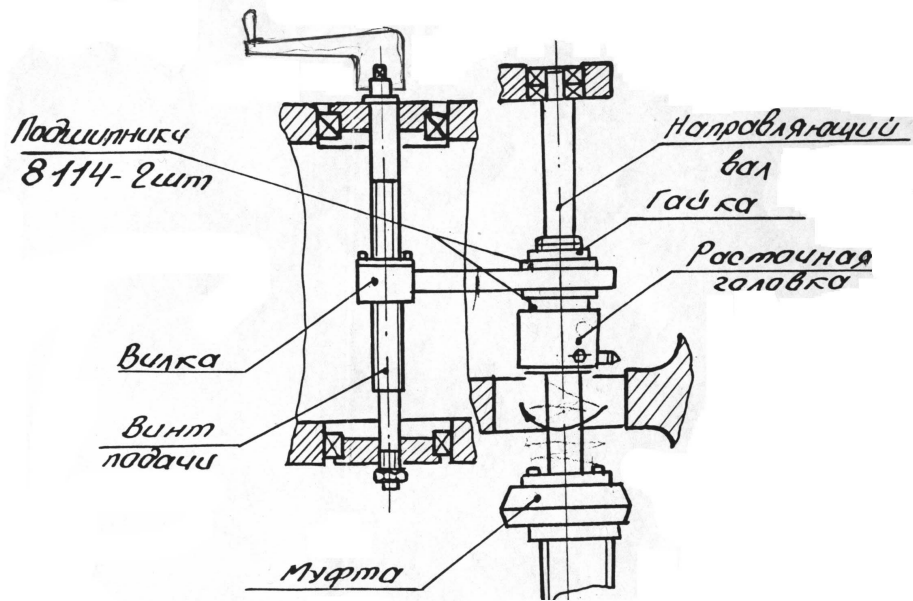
Пристосування для розточки отворів стола верстата 1К282
